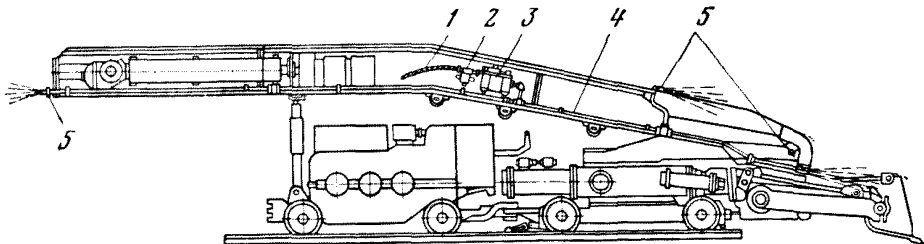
Схема оросительного устройства ковшево-конвейерной погрузочной машины типа ППН-7:
